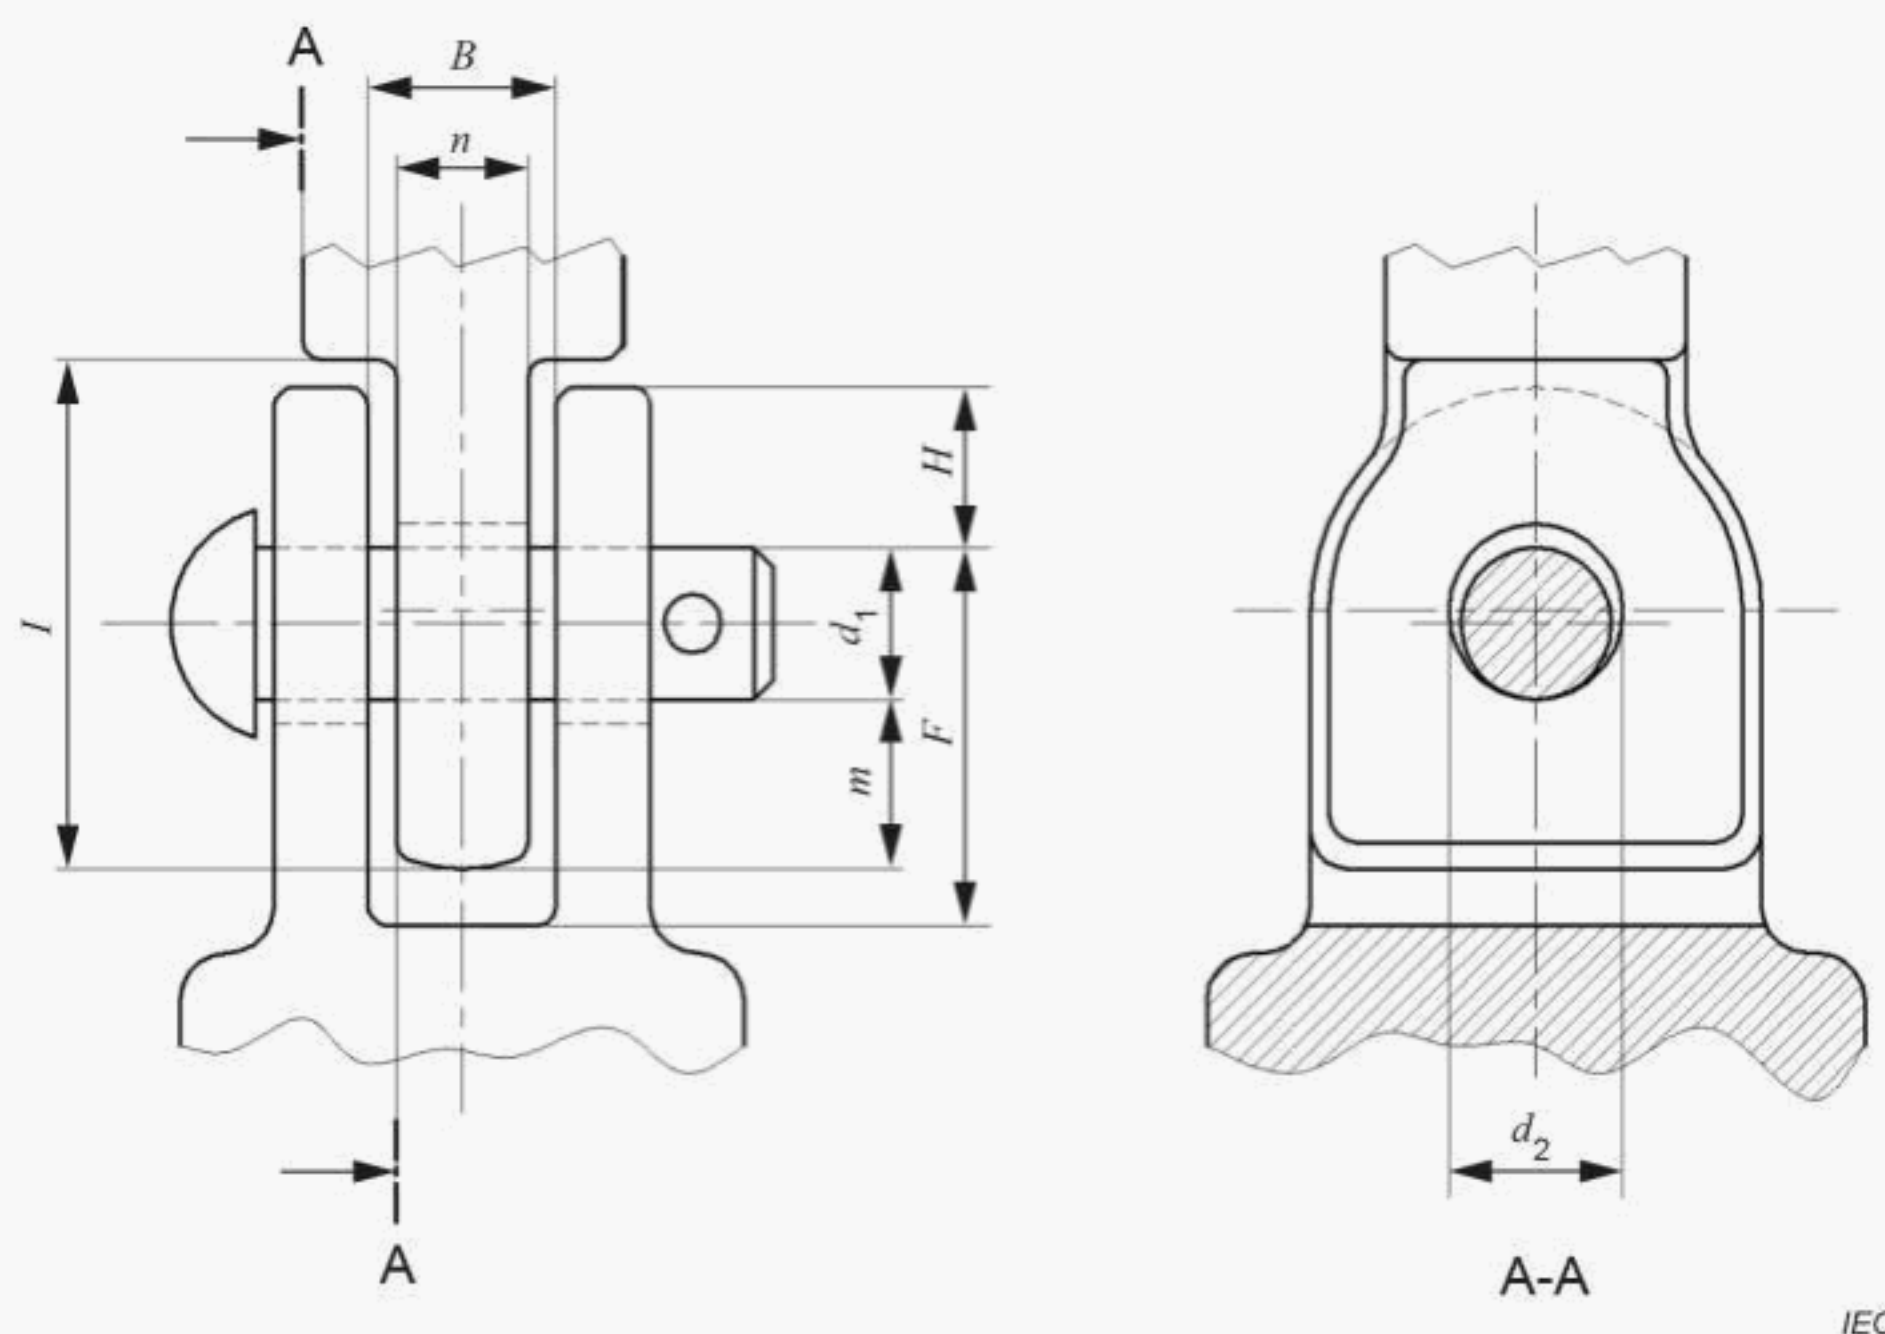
Dimensions des assemblages à chape et tenon pour les isolateurs à capot et tige
